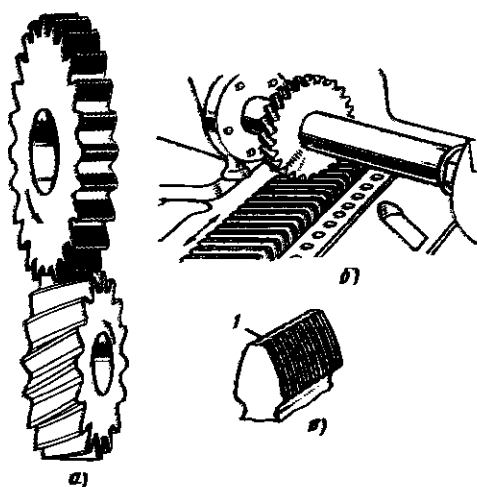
Шевингование зубчатых колес: а — дисковым шевером; б — шевер-рейкой; в — зуб шевера
